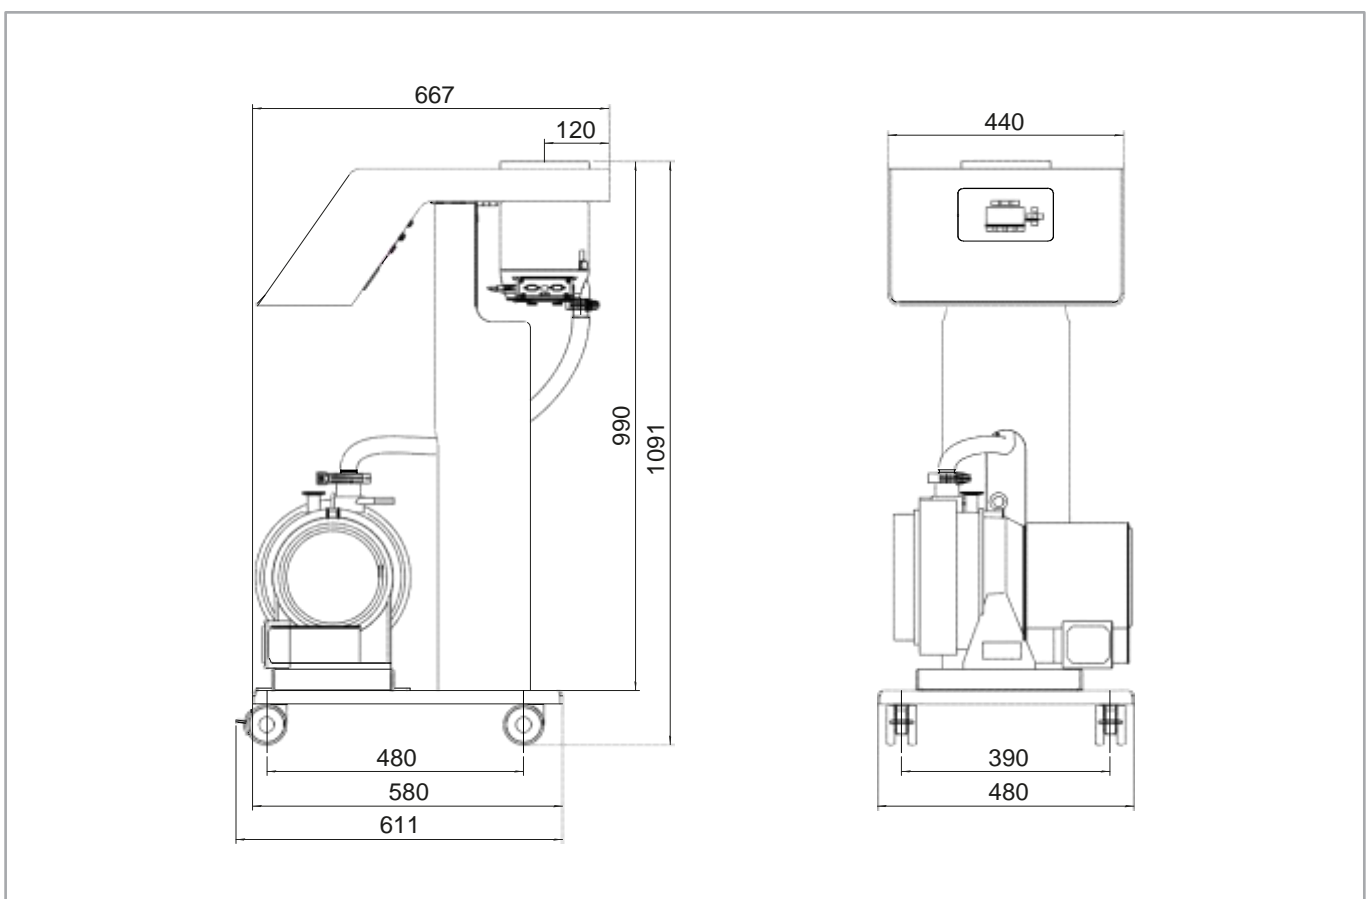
Габаритные размеры TURBOLAB 350/450 Cart, размеры в мм
